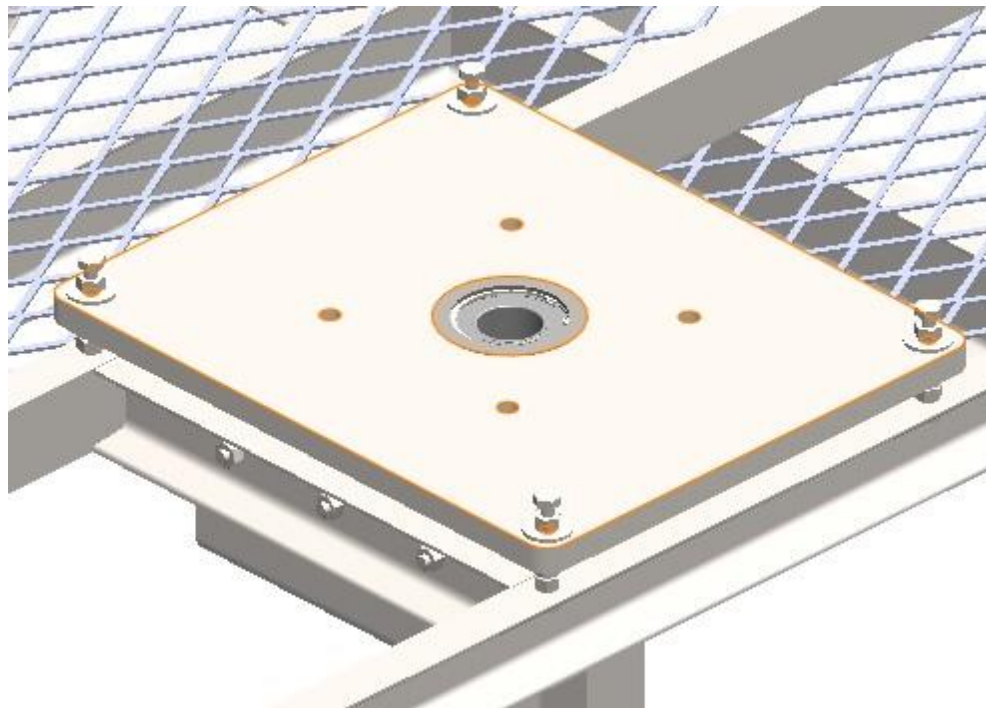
Caja de rodamiento integrada al soporte, elaboración propia.
